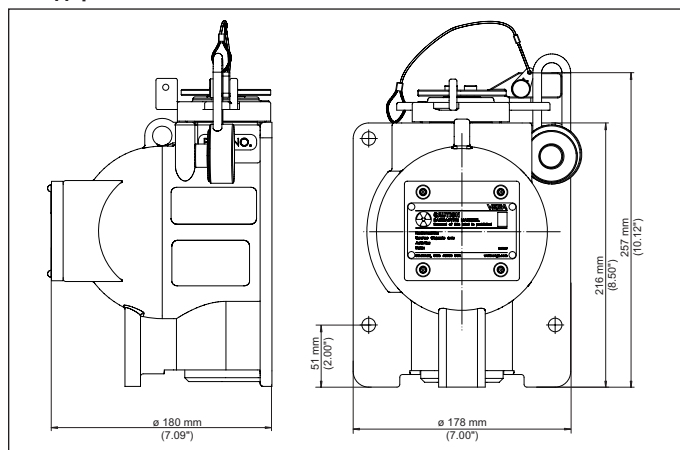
Защитный держатель источника SHLD1, стандартное исполнение
